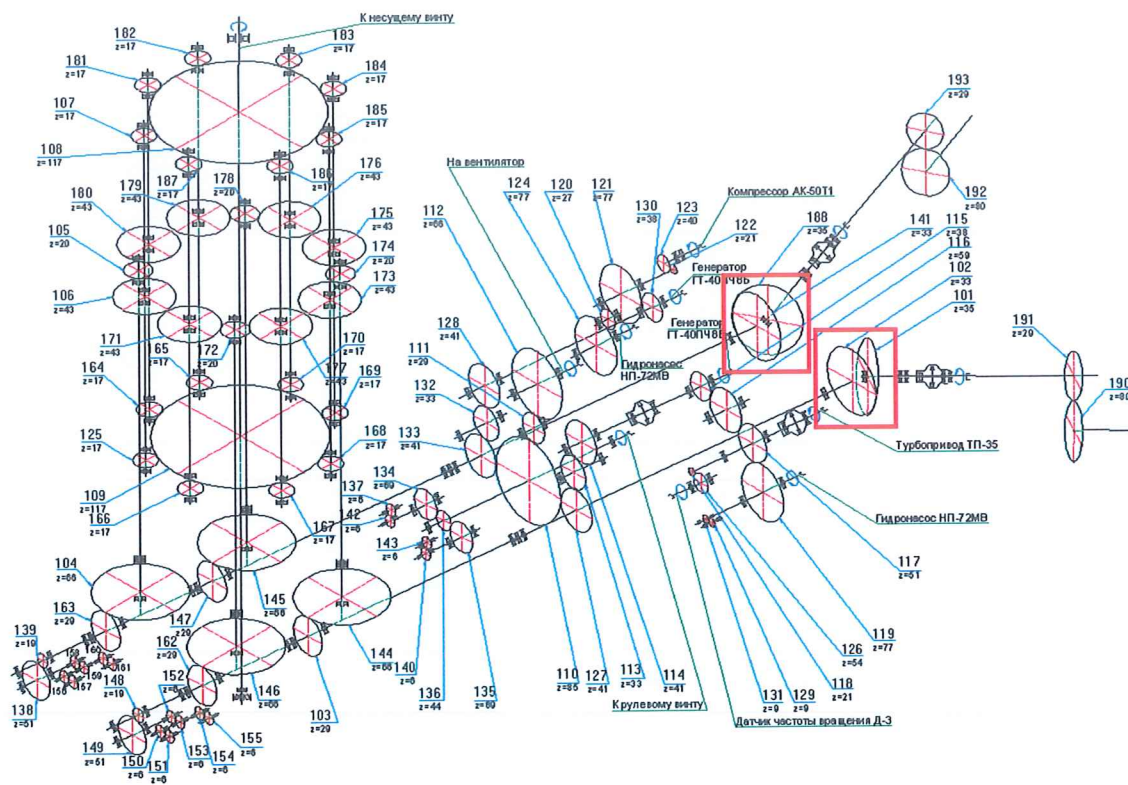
Конические передачи с круговым зубом – в кинематической схеме главного редуктора вертолета
